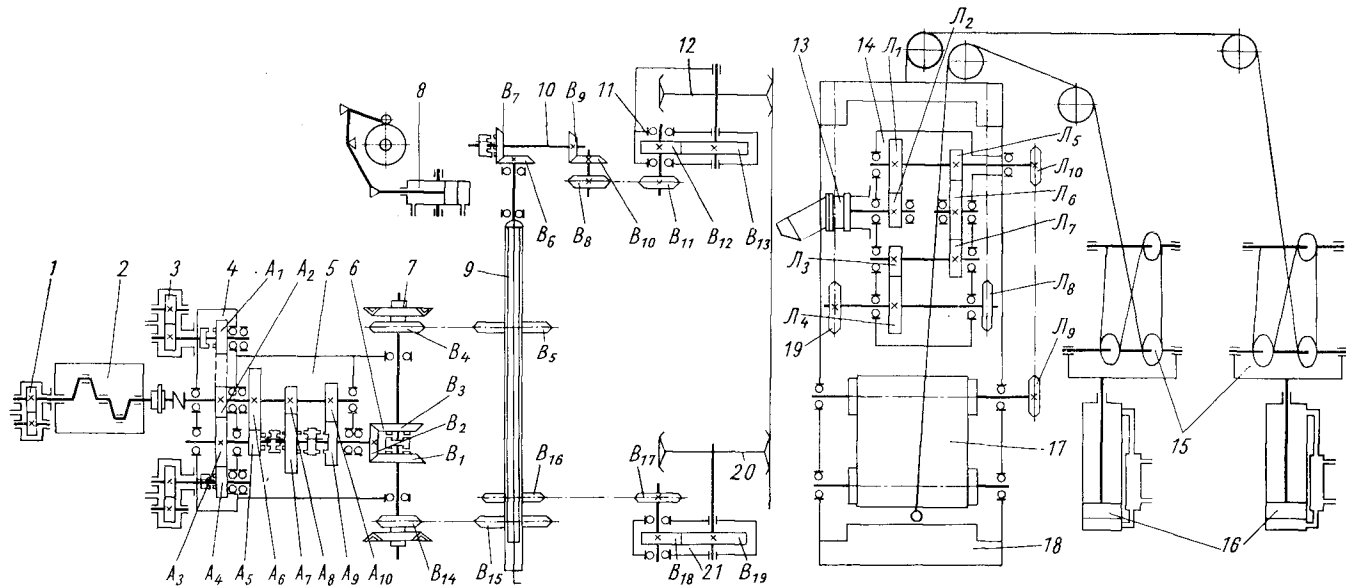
Кинематическая схема силовой передачи экскаватора ЭМ-152А:
